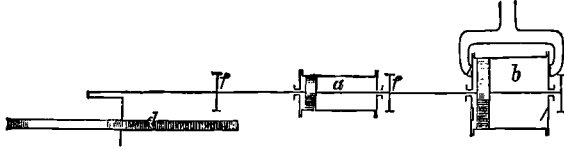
Soufflerie à vapeur horizontale à un seul cylindre.
